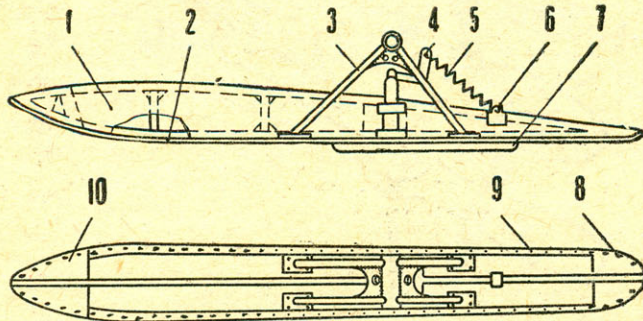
Лыжа аэросаней Т-образной формы: 1 — лонжерон лыжи; 2 — подкладка подошвы; 3 — кабанчик; 4 — тормозной механизм; 5 — пружина тормозного рычага; 6 — узел крепления пружины; 7 — подрез; 8 — задняя оковка; 9 — окантовочный угольник; 10 — оковка носовой части.
